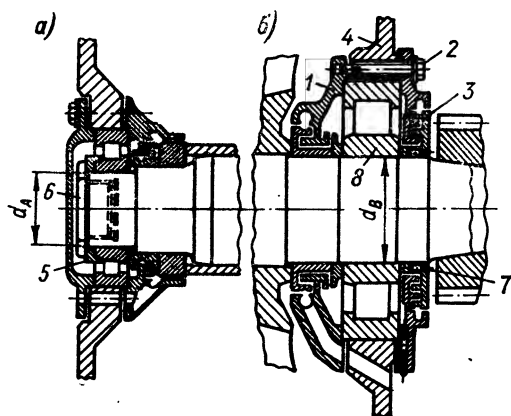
Роликоподшипники тягового двигателя: а — с фасонным кольцом в переднем подшипниковом щите; б — с внутренними бортами на наружном кольце со стороны зубчатой передачи
